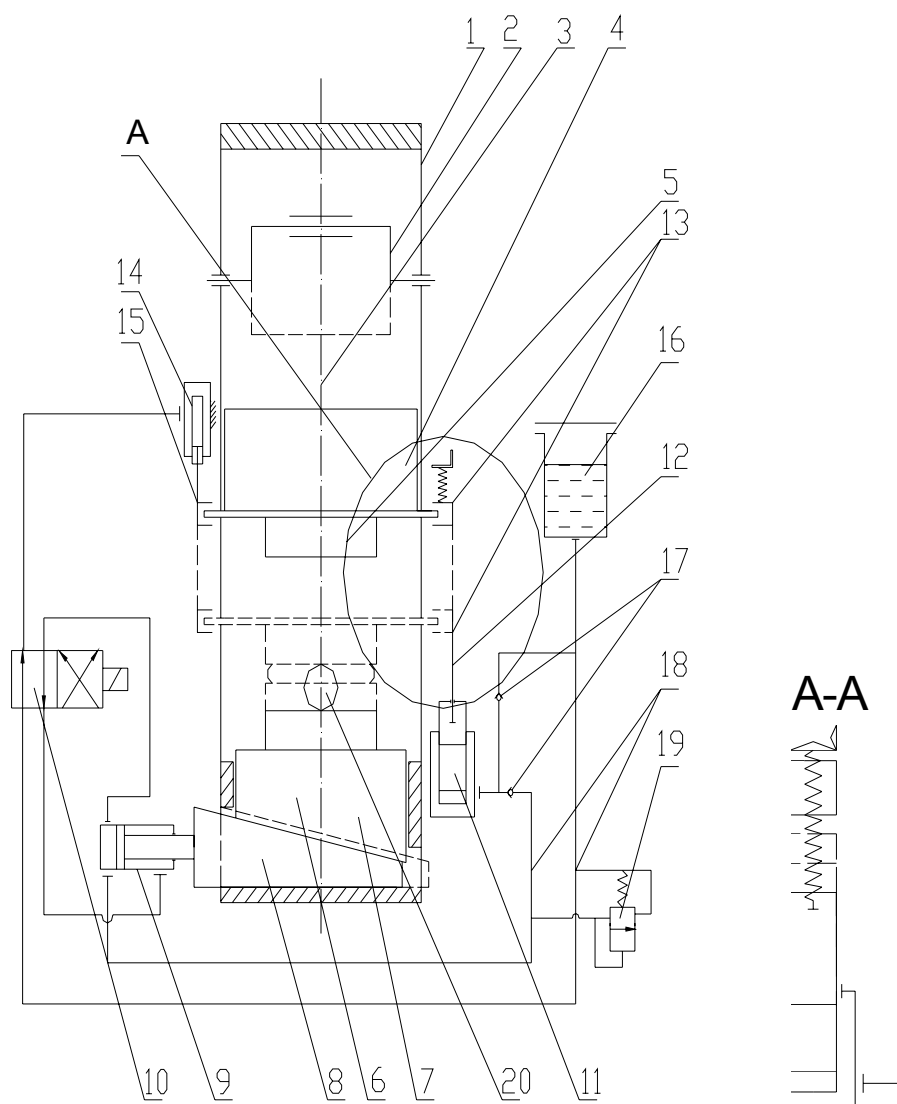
Схема кривошипного пресса с кинематической (гидравлической) связью ползуна и стола
